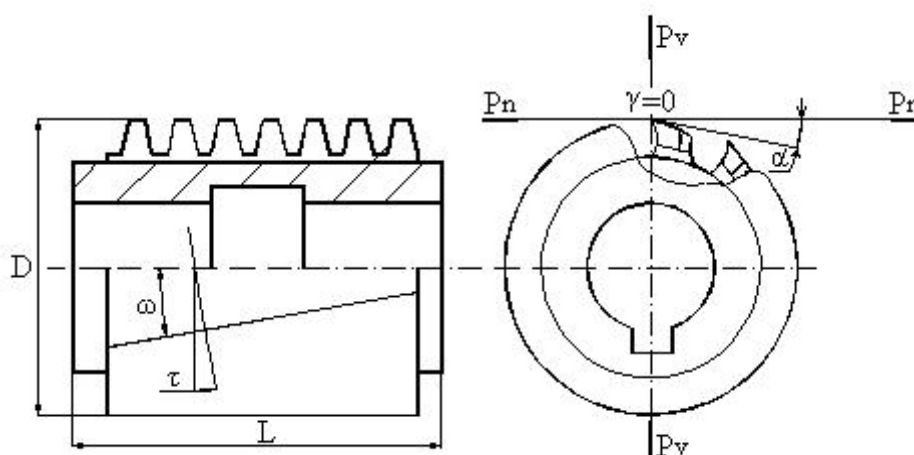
Конструкция и геометрические параметры червячной фрезы
